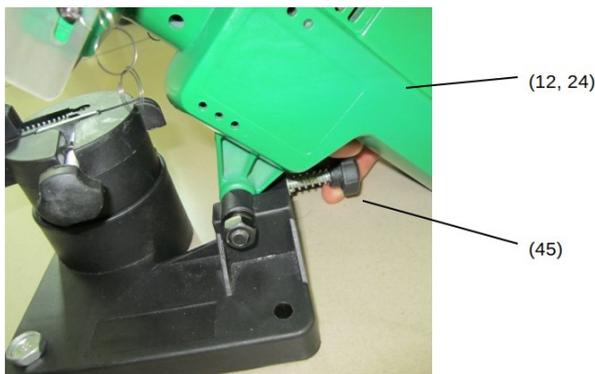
Motoregehäuse (12, 24) und Einstellschraube (45)
